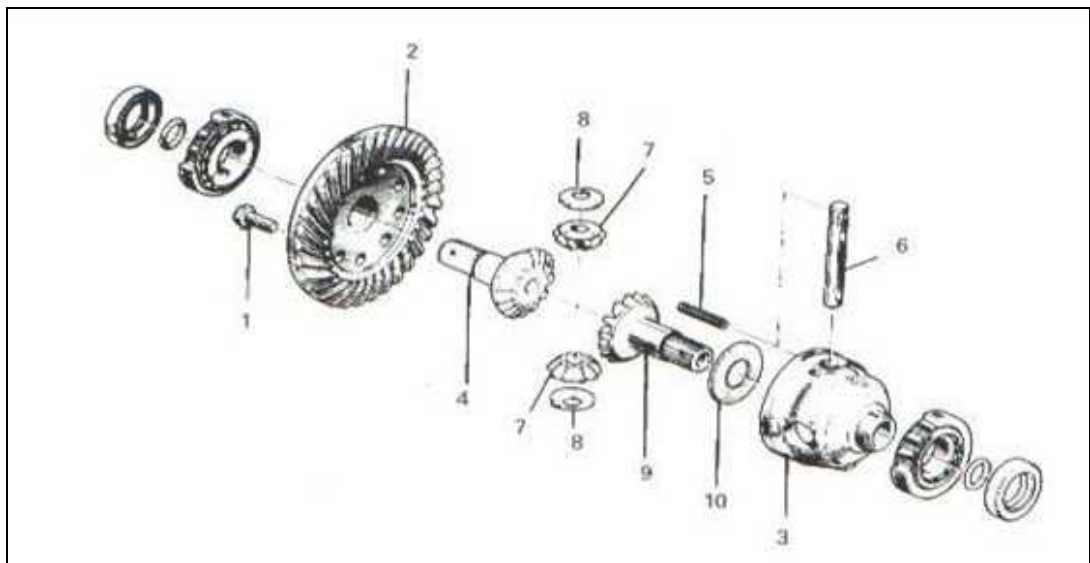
14: Despiece explosionado de un diferencial mecánico libre
